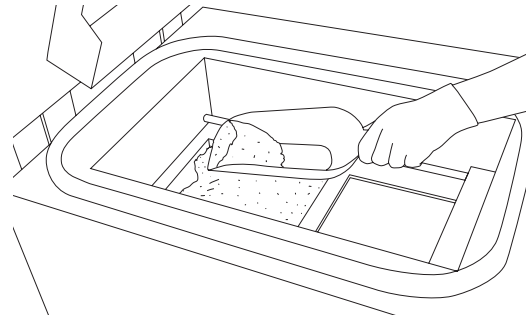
Entfernen des Pulvers aus dem VORSCHUBBETT.
